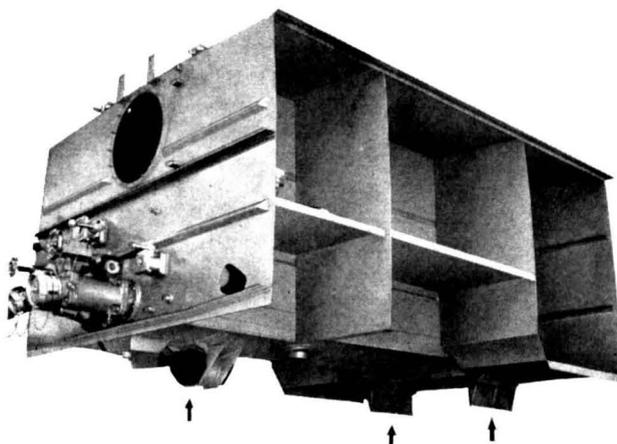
Selbsttragender Tankaufbau mit Dreipunktlagerung
